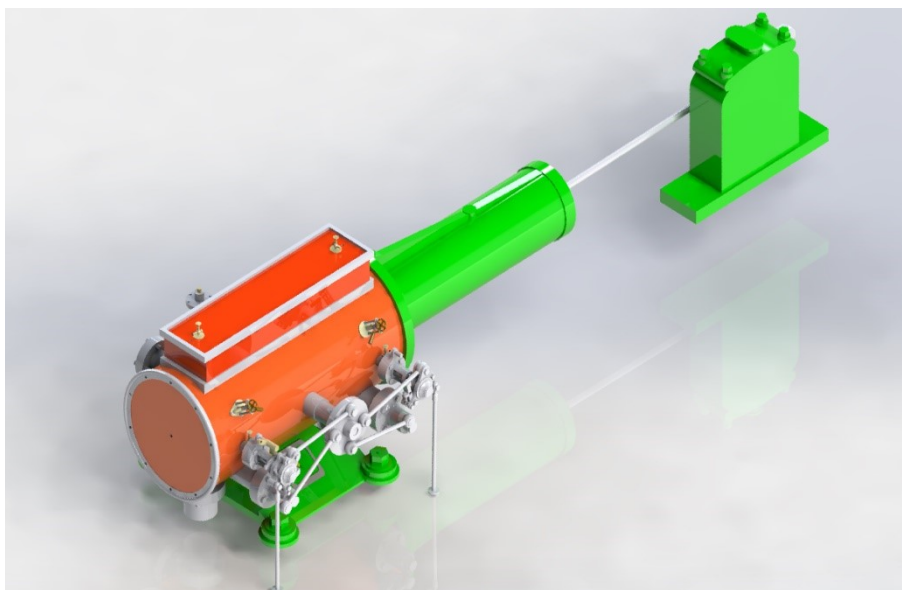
Vista em perspectiva do conjunto das partes (fotorrealismo)
